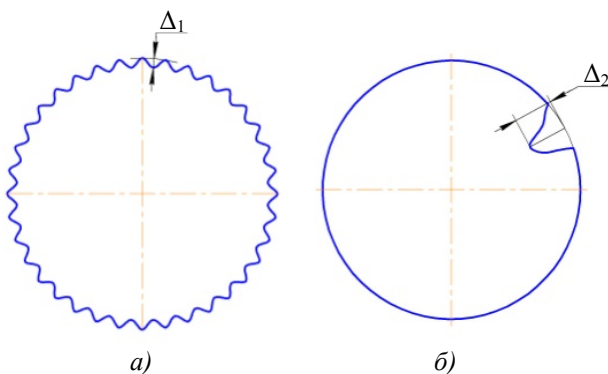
Профиль поперечного сечения цилиндрической поверхности детали:
